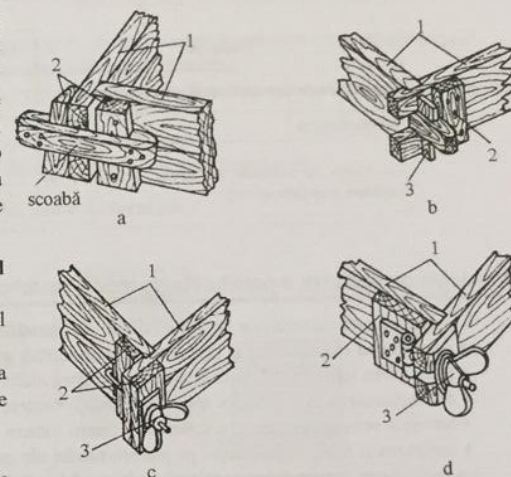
Sisteme de lemn pentru îmbinarea demontabilă a cutiilor de miez: a - cu scoabe de lemn; b - cu pene din lemn; 1 - pereții cutiilor; 2 - întăritori; 3 - pene; c - cu șurub cu cap cârlig; d - cu șurub cu balama; 1 - pereții cutiei; 2 - întărituri; 3 - dispozitiv de strângere.
